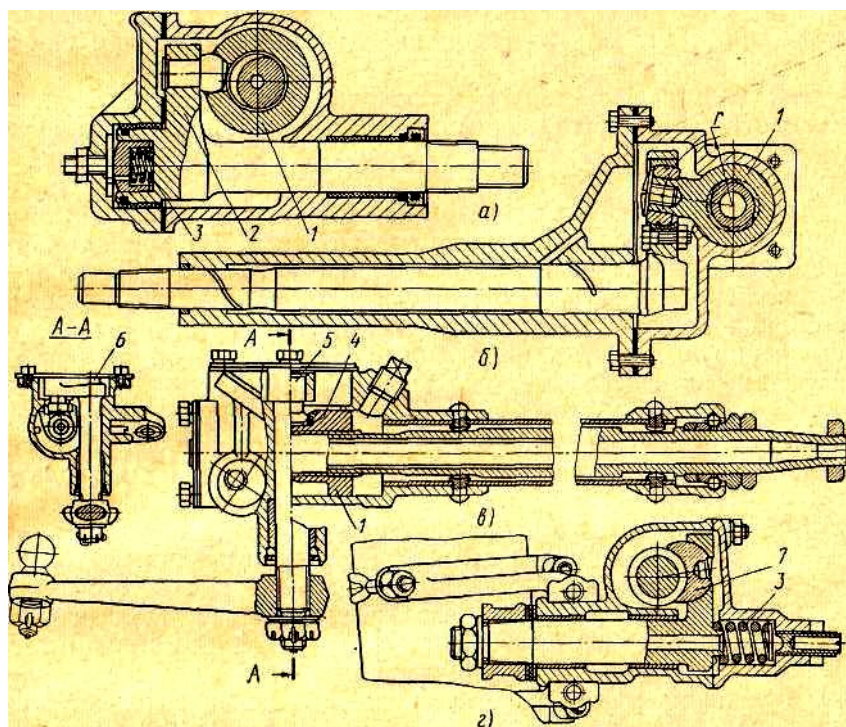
Рулевые механизмы с винтовой передачей и поворачивающейся гайкой
